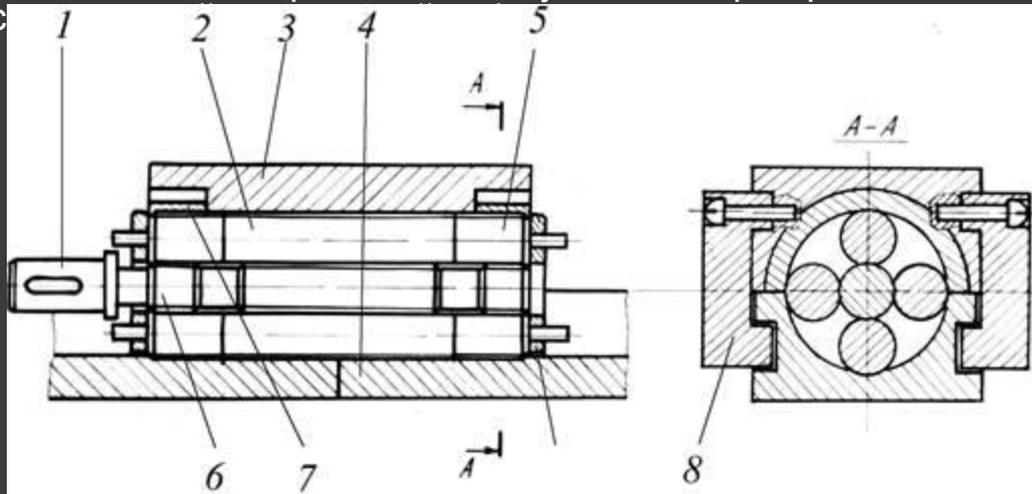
Червячно-реечная передача с резьбовыми роликами: 1 – винт; 2 – резьбовые ролики; 3 – полугайка опорная; 4 – полугайка-рейка; 5 – зубчатые венцы роликов; 6 – зубчатые венцы винта; 7 – полувенцы; 8 – сепараторы; 9 – прижимные планки
